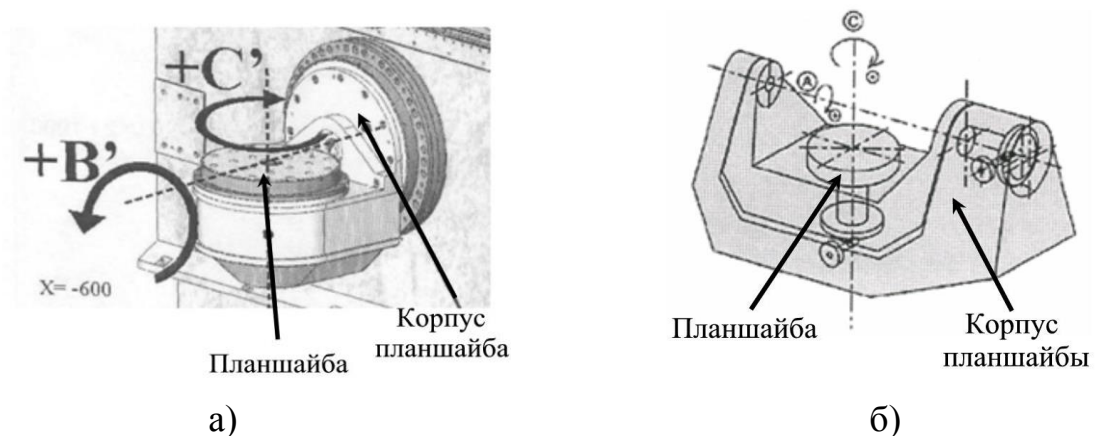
Поворотные столы: а) консольный поворотный стол станка мод. МС - 300, б) двухопорный поворотный стол станка мод. МС - 700
